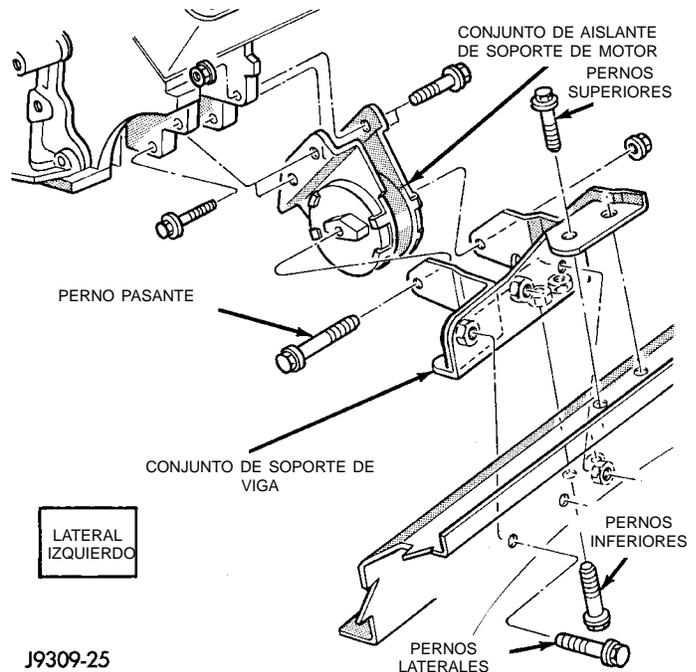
Soporte delantero del motor—Lateral izquierdo
